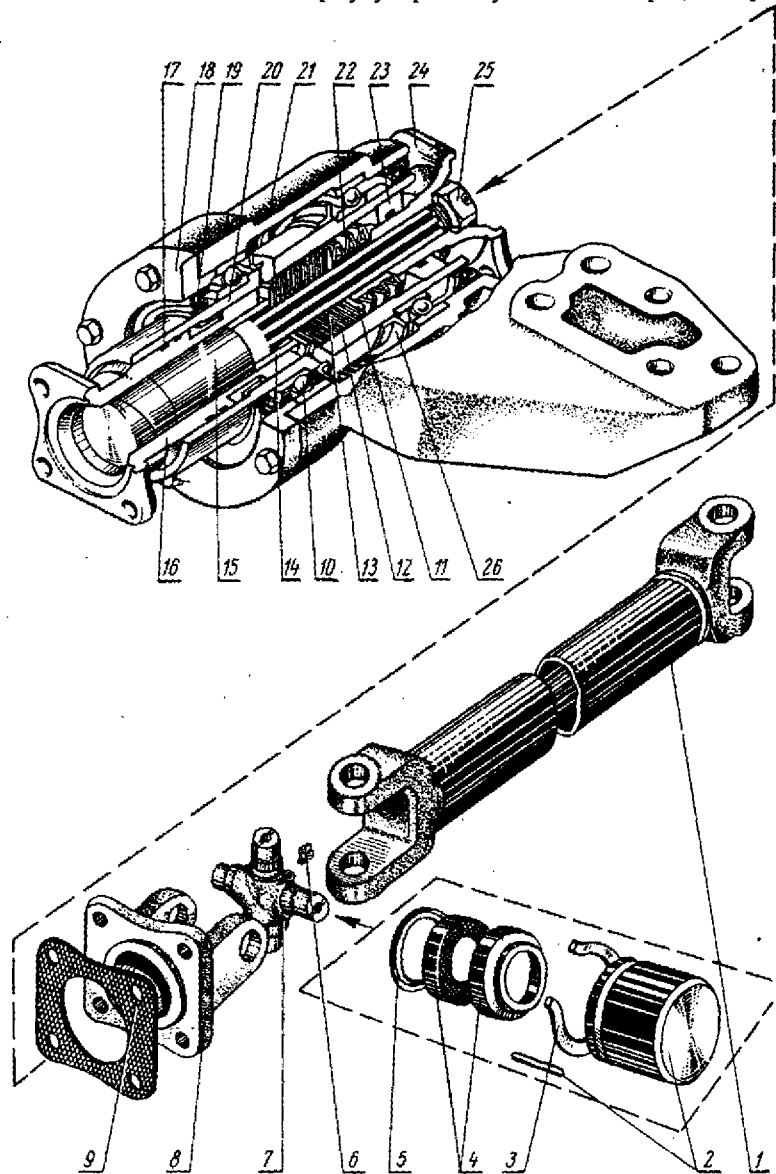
Карданный привод переднего ведущего моста с промежуточной опорой полноприводных тракторов МТЗ и ЮМЗ: 1 – карданный вал; 2 – игольчатый подшипник; 3 – стопорное кольцо; 4 – сальник крестовины в сборе; 5 – отражатель сальника карданного вала; 6 – пресс-масленка; 7 – крестовина; 8 – фланец кардана; 9 – прокладка; 10 – подшипник; 11 – нажимной диск; 12 – ведомый диск; 13 – ведущий диск; 14 – распорная втулка; 15 – вал промежуточной опоры; 16 – фланец скользящей; 17 – уплотнительные кольца; 18 – корпус манжеты; 19 – манжеты; 20 – втулка муфты; 21 – корпус промежуточной опоры; 22 – тарельчатые пружины; 23 – опорная шайба; 24 – соединительный фланец карданного вала; 25 – гайка; 26 – маслоотражательная шайба
